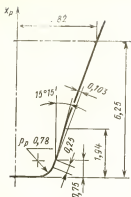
Профиль инструментальной рейки для колеса, подлежащего шевингованию
